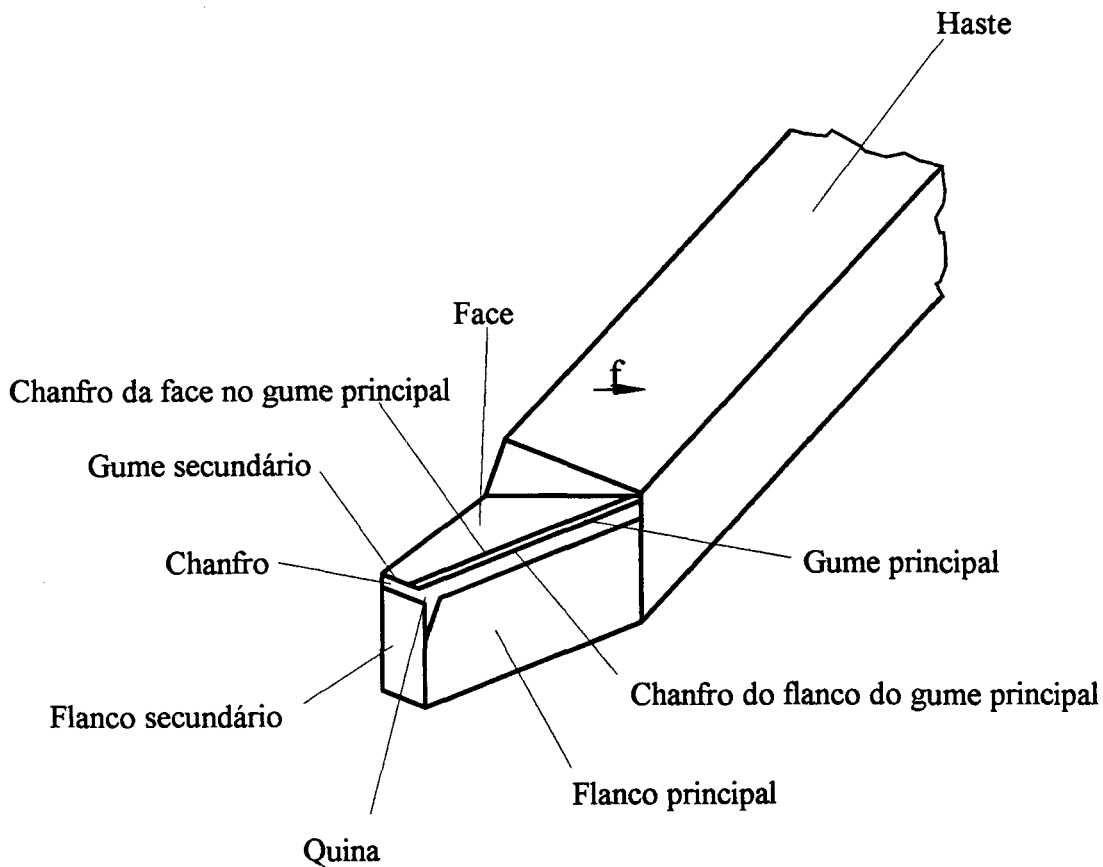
Esquema representativo de uma ferramenta com geometria de corte definida
